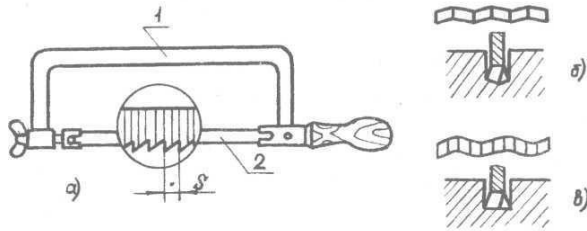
Ножовочный станок и виды разводки зубьев ножовочного полотна.
